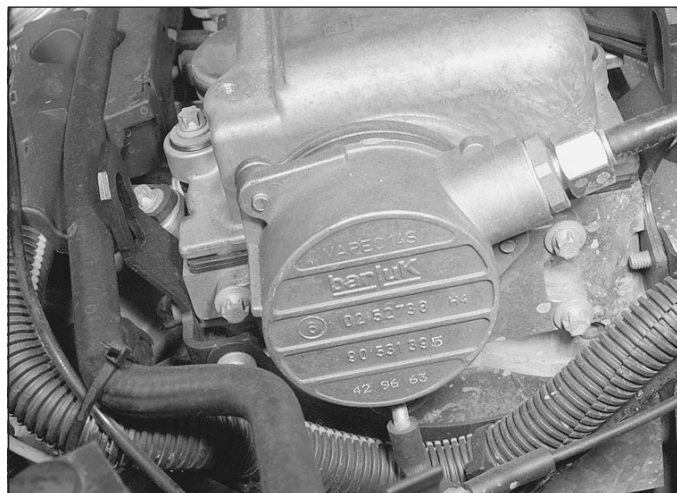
Вакуумный насос на левой стороне головки цилиндров – двигателя 2.0 л
